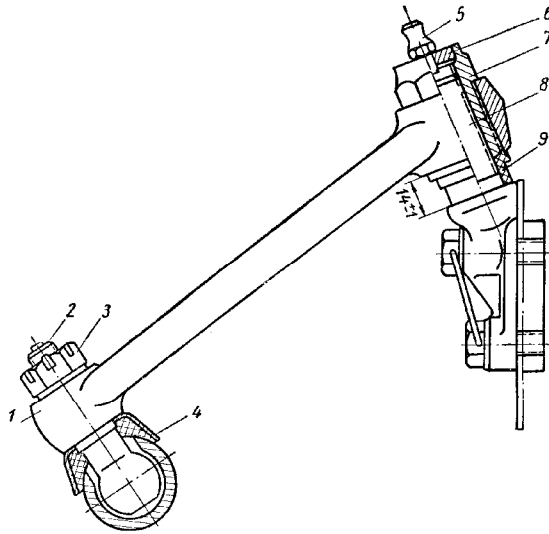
Соединение верхнего конца стойки подвески с рычагами амортизатора:
